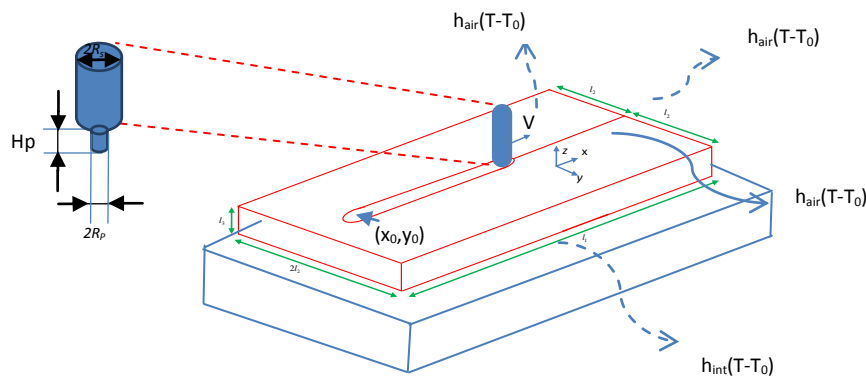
Schématique des pièces soudées et du système de serrage.
